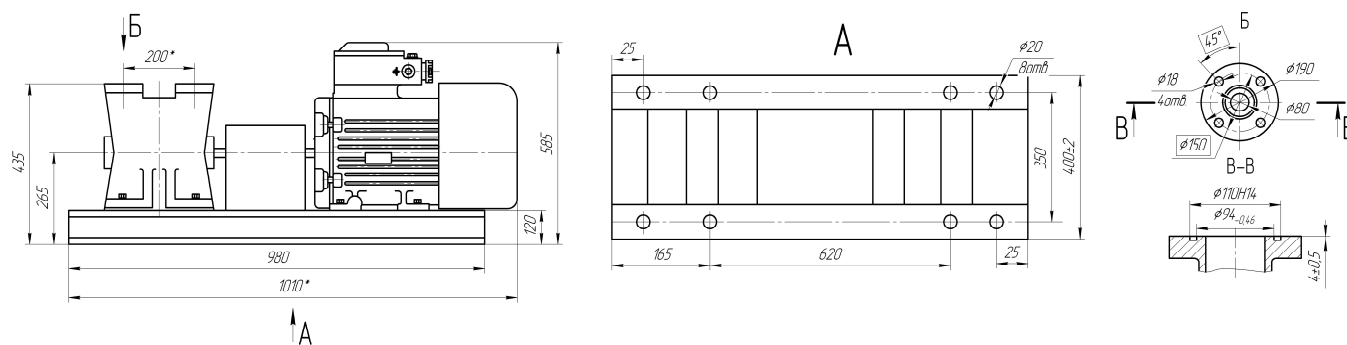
Габаритные и присоединительные размеры АСВН-Е
